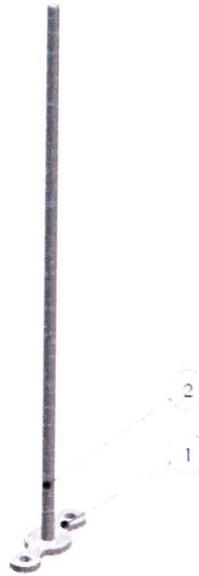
Anschlagseinrichtung, Typ: ZS 300-800 II B / B-S
